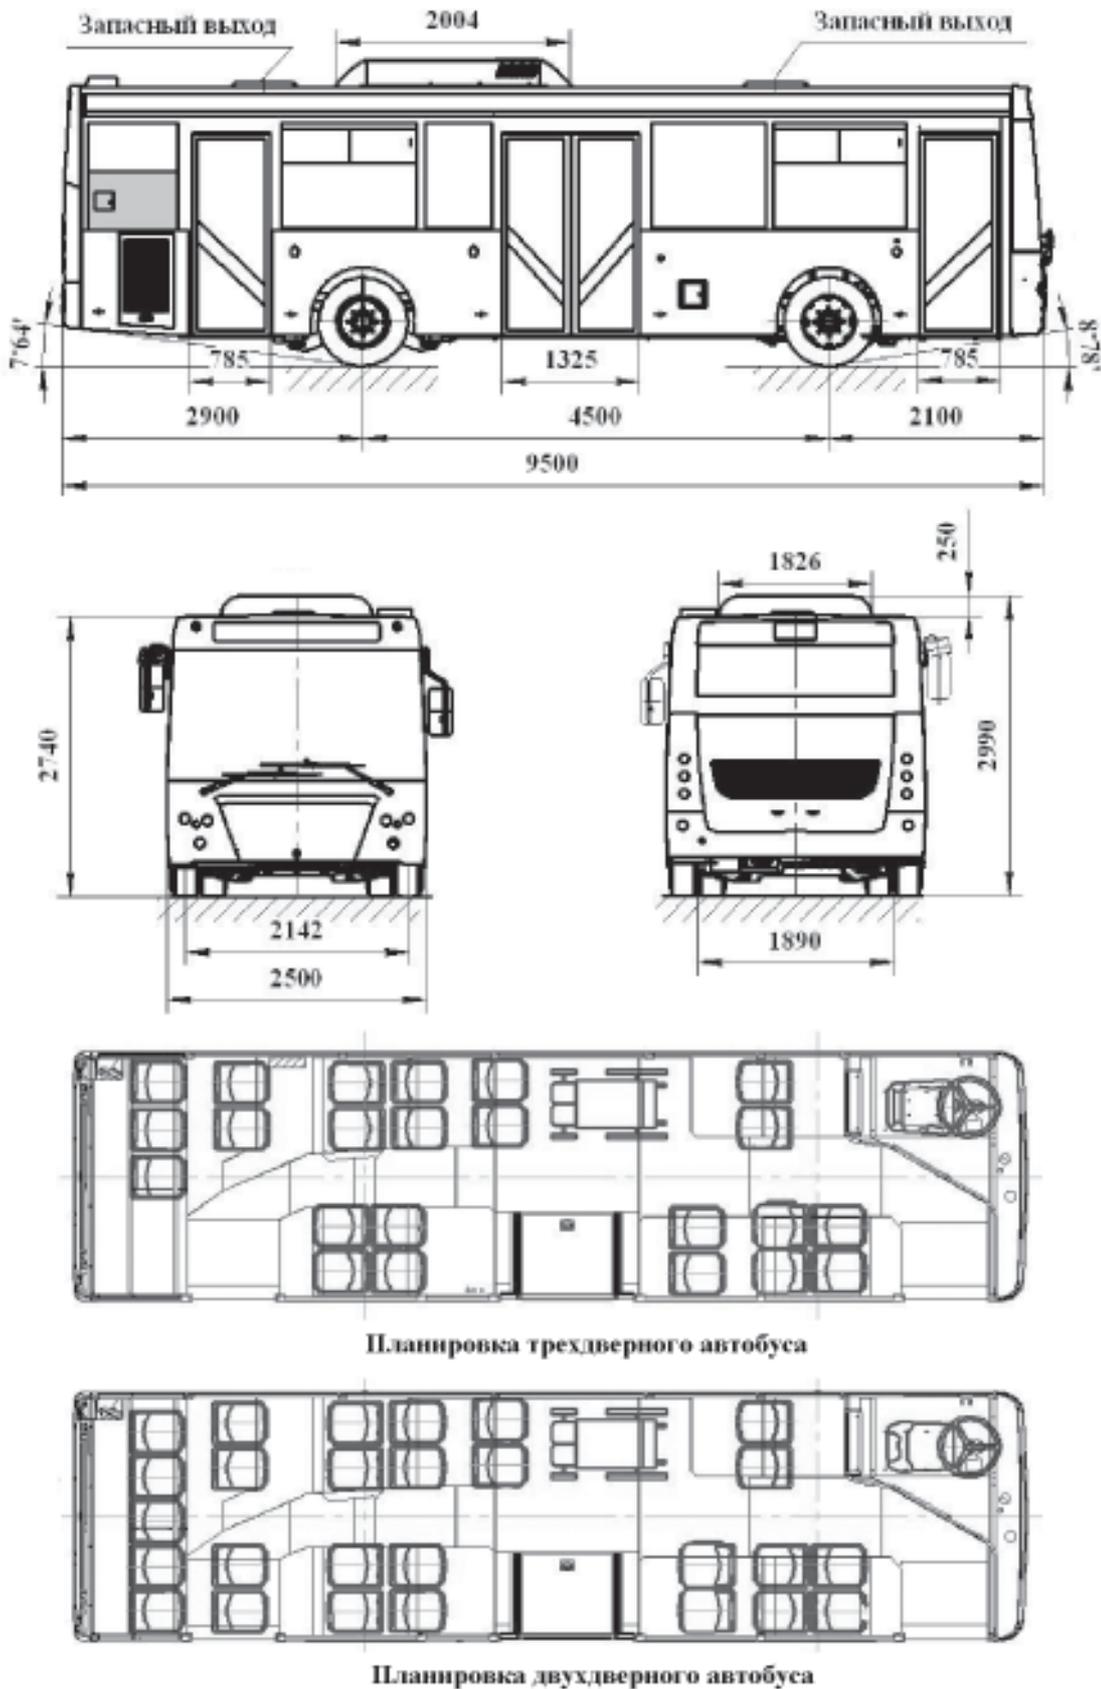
Габаритные размеры автобусов ЛиАЗ-429260-79
